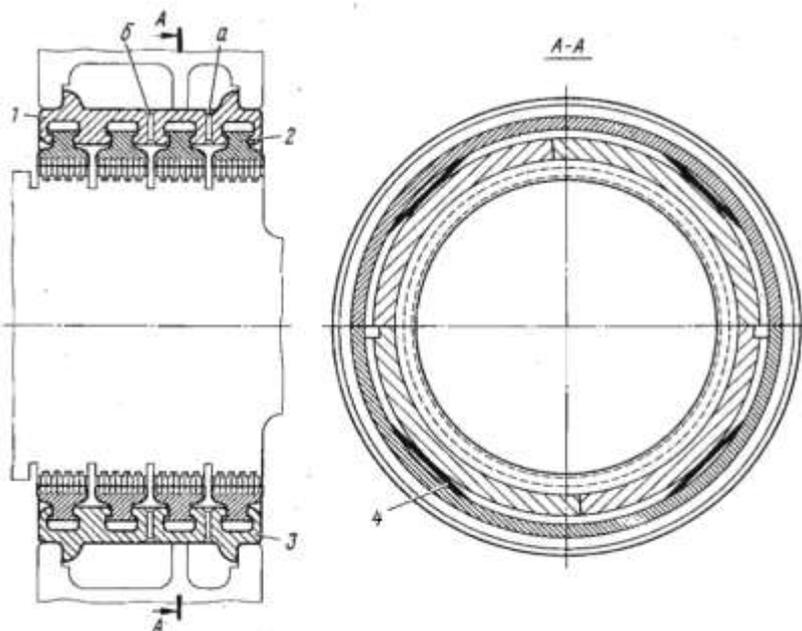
Уплотнительная коробка турбины ПТГ ТД-400
